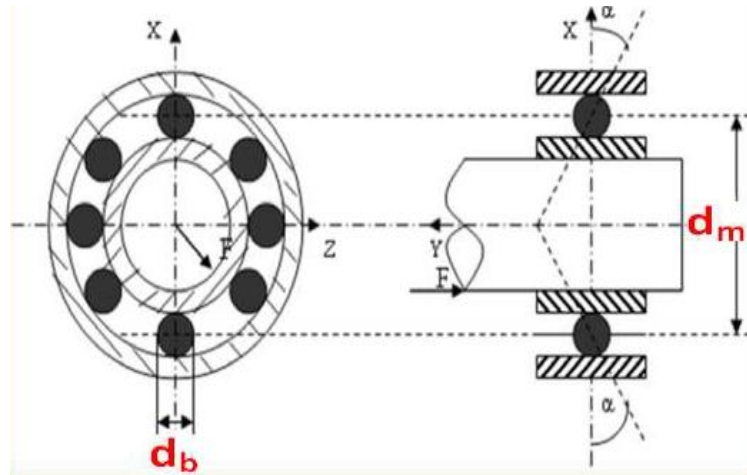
Géométrie et dimensions d'un roulement. [24]
